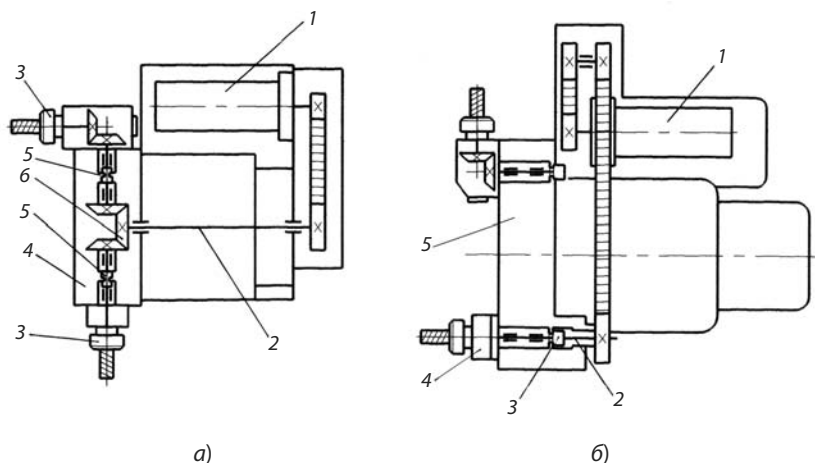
Примеры конструктивных схем вращения инструментов в револьверных головках:
